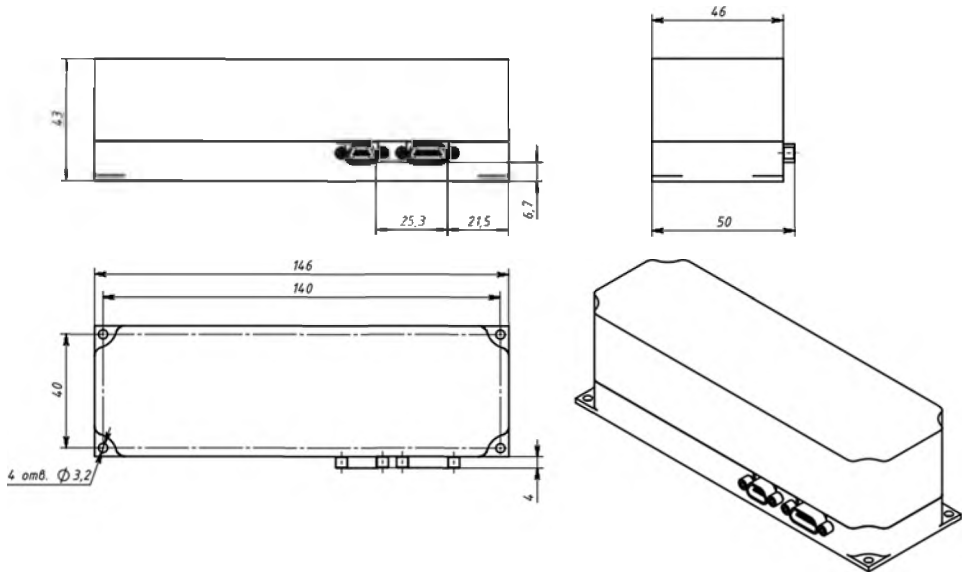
Габаритный чертёж гироина SX-CMG-01
